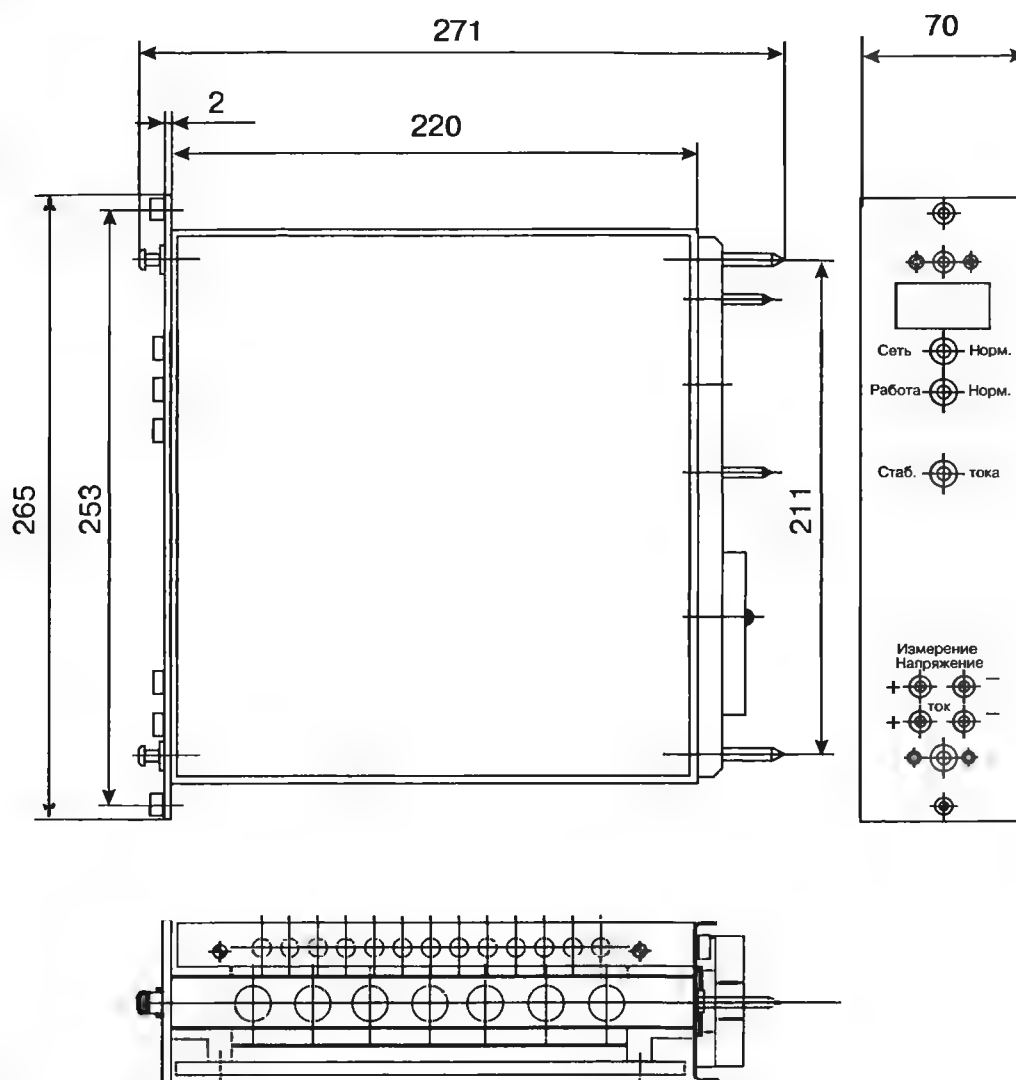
Общий вид блока БПС-30В/10А-Т и его габаритные размеры
